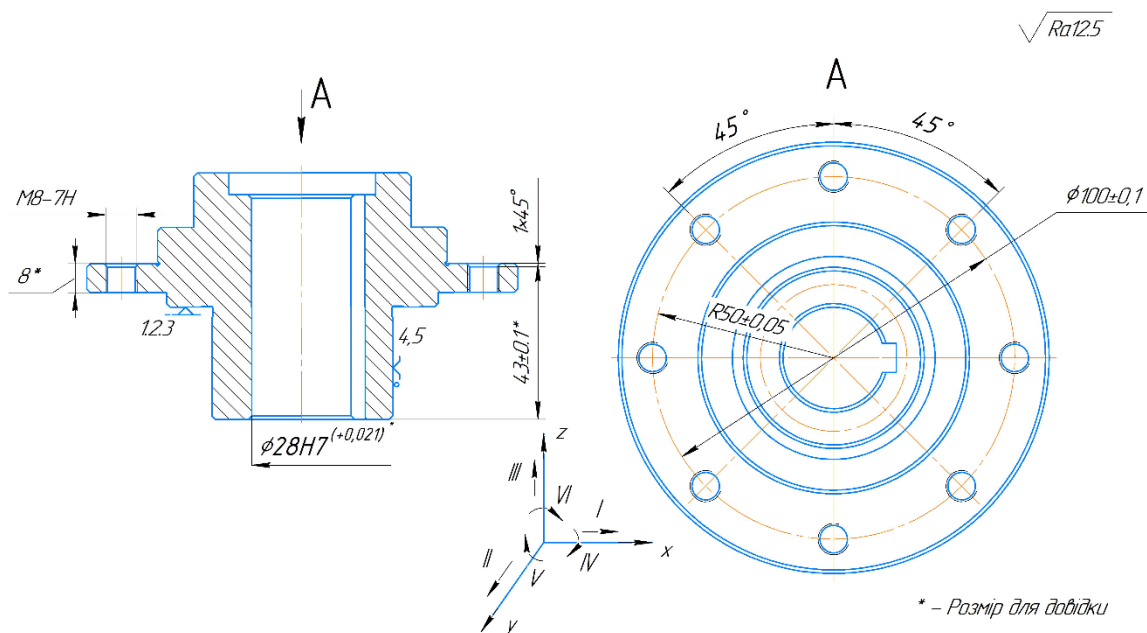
Схема базування заготовки на операції 040. Варіант №2
